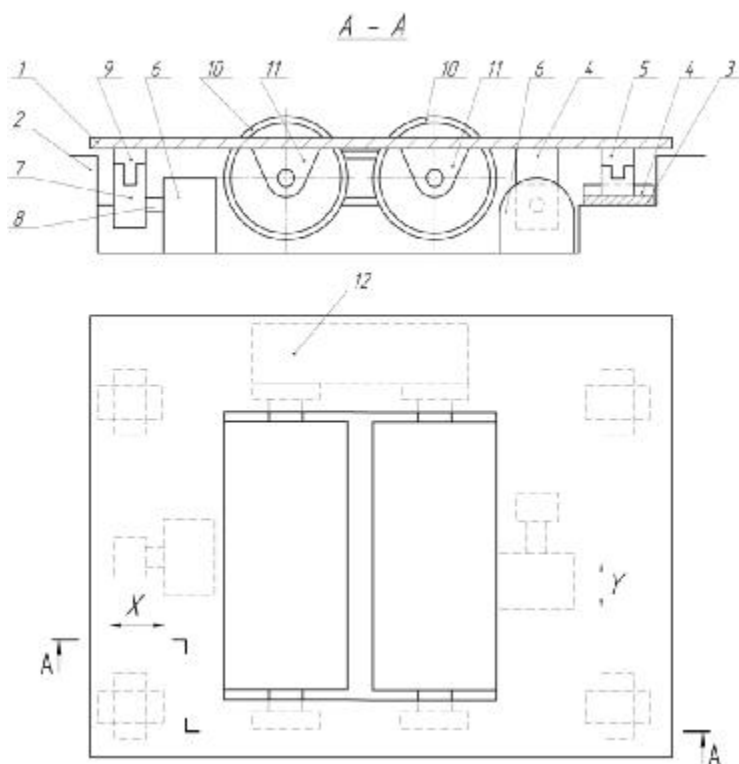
Внешний вид стенда диагностики ступичного подшипника
